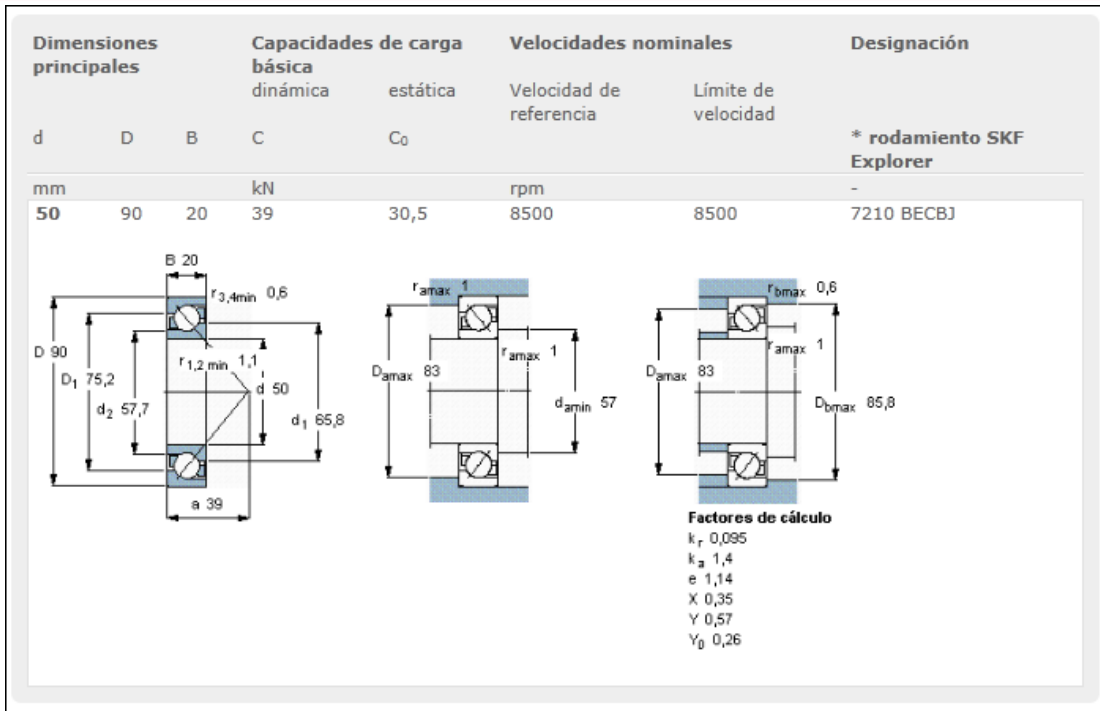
Ficha técnica del rodamiento 7210 BECBJ
